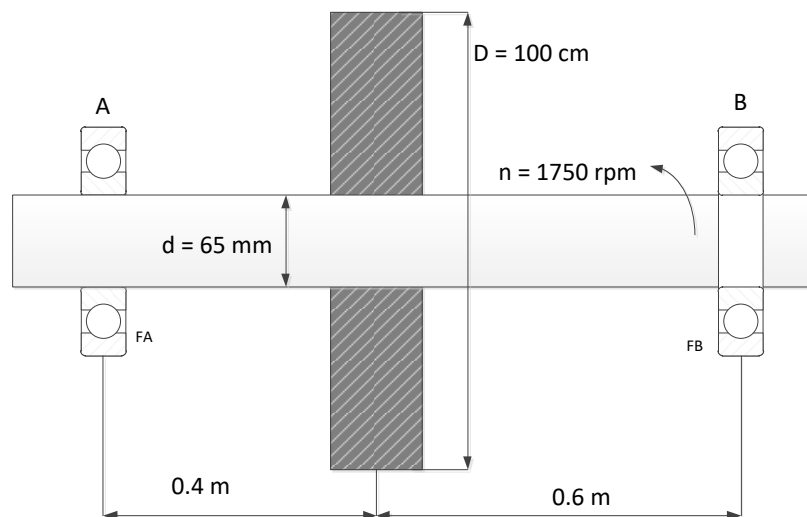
Montaje de rodamientos y rotor en bomba de agua al molino principal
